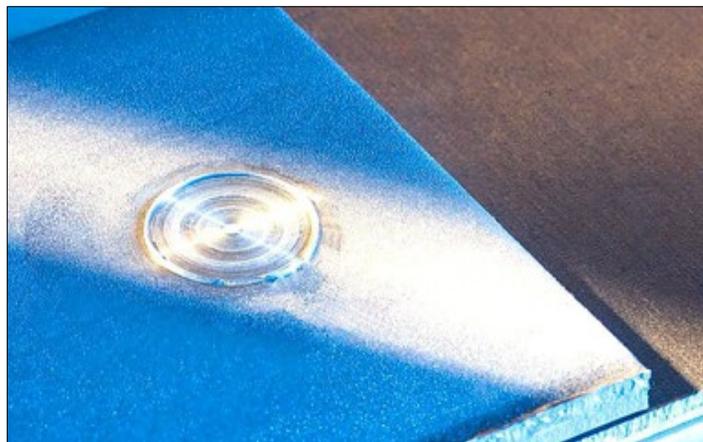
soudage friction spot de l'aluminium sur l'acier (source: Riftec gmbh)
